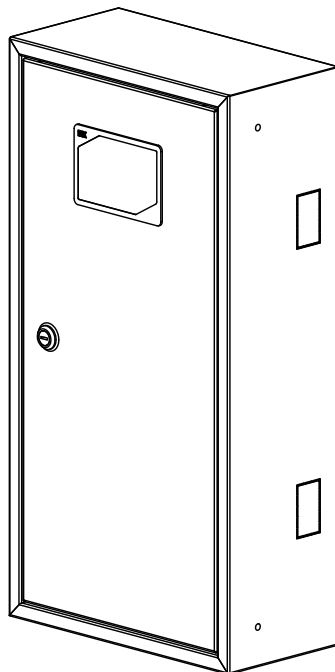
Общий вид корпуса ЯУР-3/12
